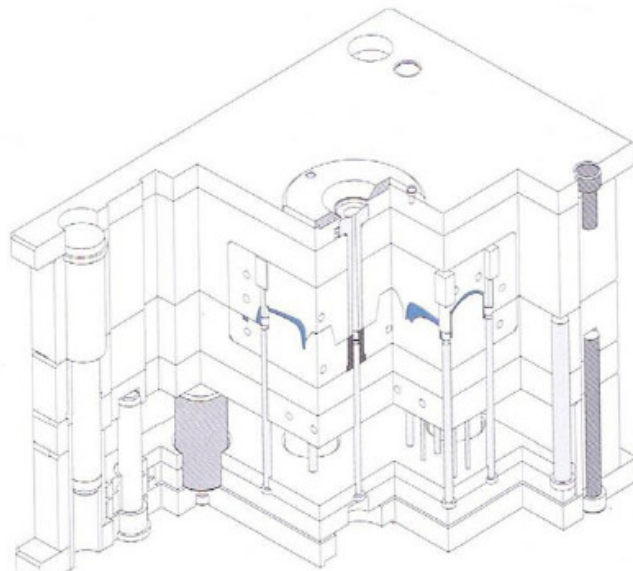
Vista em corte de um molde simples. (BRITO (2004))
